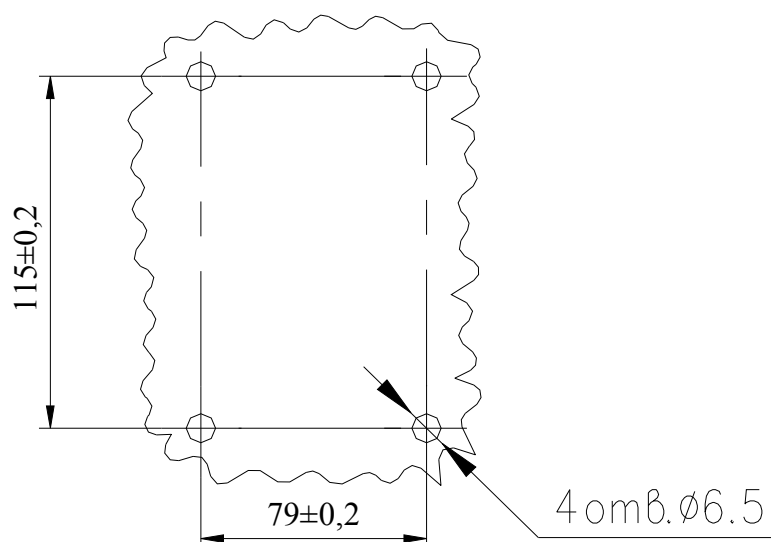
Габаритный чертеж и разметка панели под установку Блок БС-4
